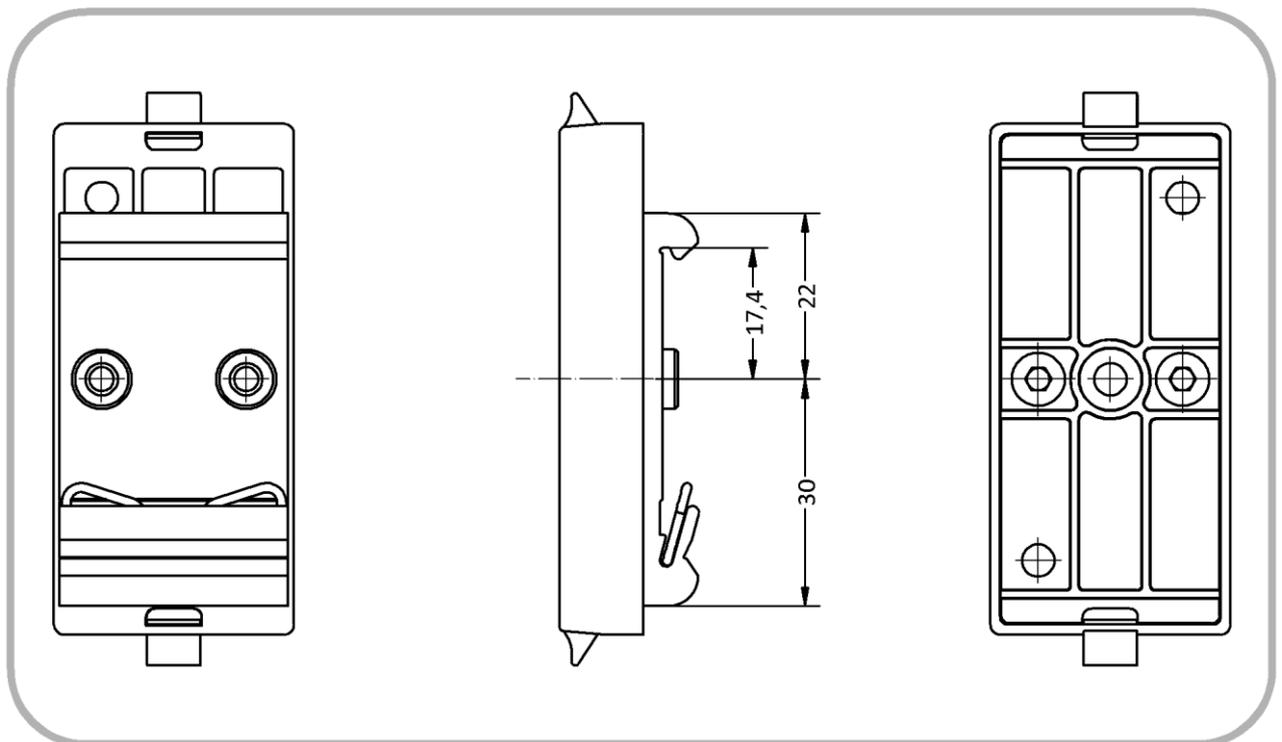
Maßzeichnung Z-6R. Alle Maßangaben in Millimetern.
